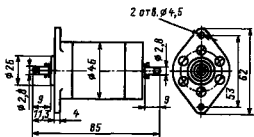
42 Габаритные и установочные размеры двигателя ШД-300-300
